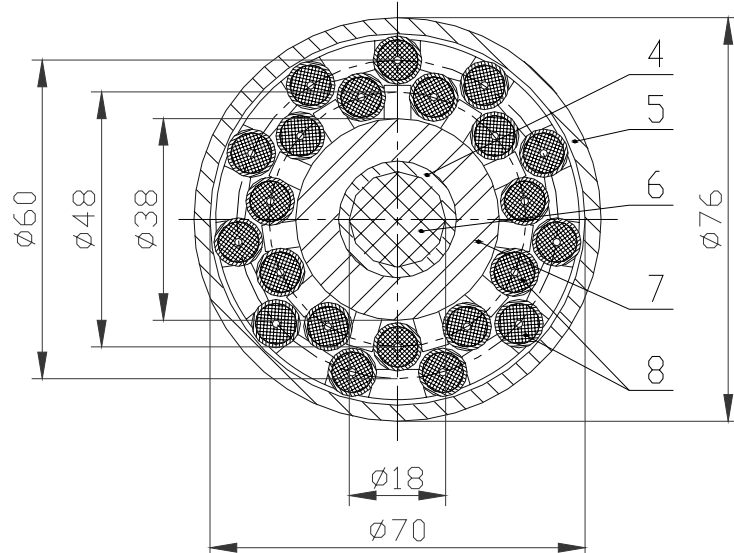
Поперечный разрез ТК реактора ИВГ1.2М в районе активной зоны: 4 – труба для установки поглотителя нейтронов, 5 – корпус ТК, 6 – поглотитель нейтронов, 7 – бериллиевый вытеснитель, 8 – ТВЭЛ
